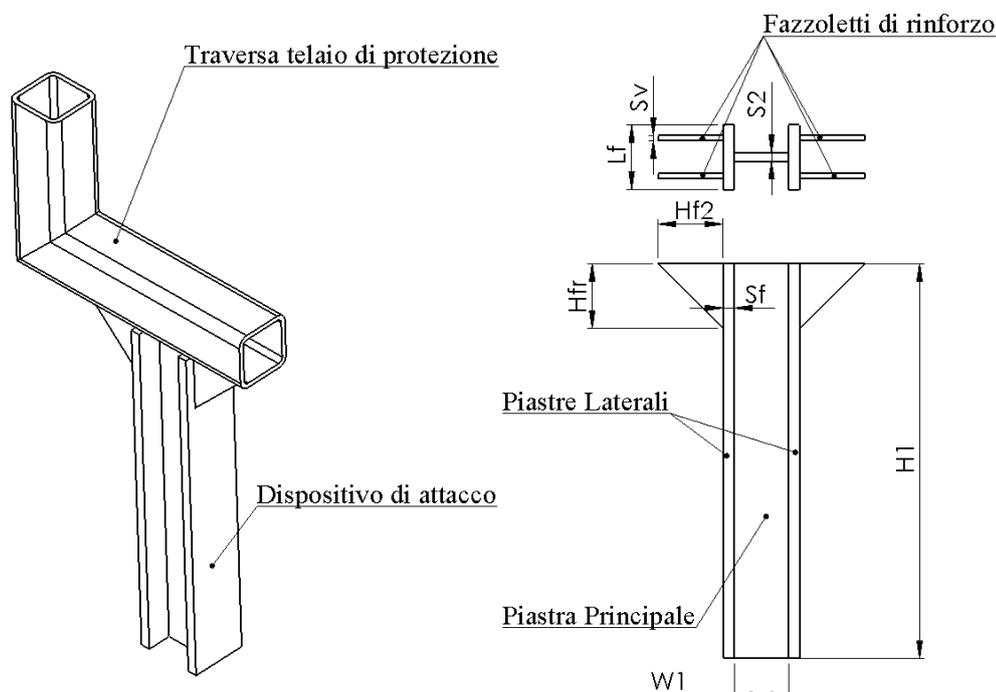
Dimensioni del dispositivo di attacco di classe *D*.
